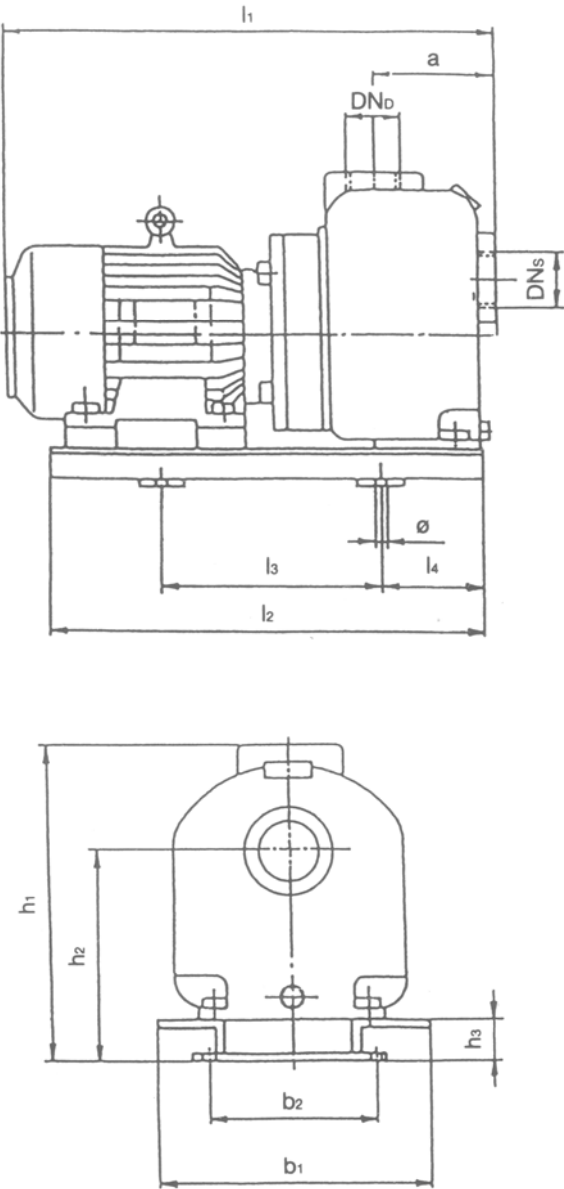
Габаритный чертёж насоса типа РО 32BL,
